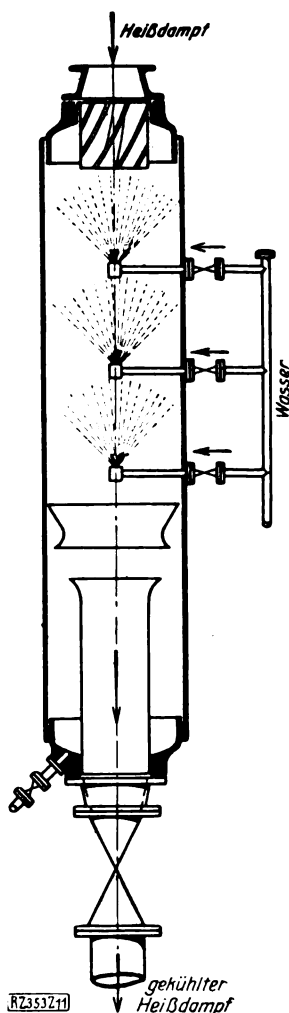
Heißdampfkühler mit Wassereinspritzung.
